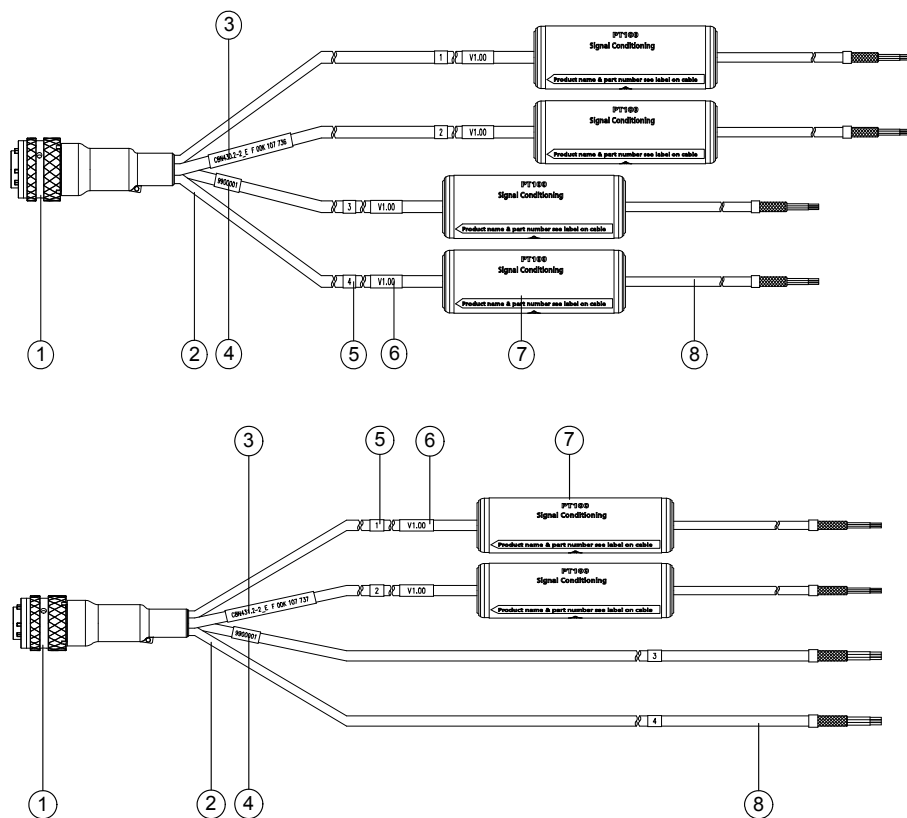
Aufbau des Sensorkabels CBN430.2/ CBN432.2/ CBN434.2 (oben) und CBN431.2/ CBN433.2 (unten)
